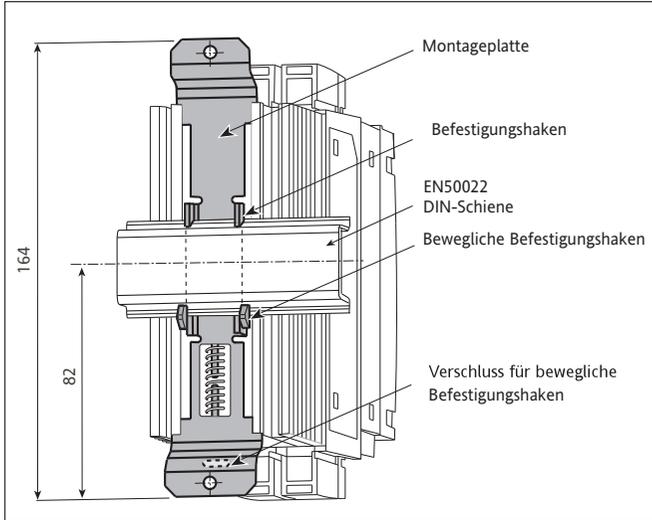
Montage des 7100A Thyristorstellers auf DIN-Schiene (16 A bis 63 A, Rückansicht)
